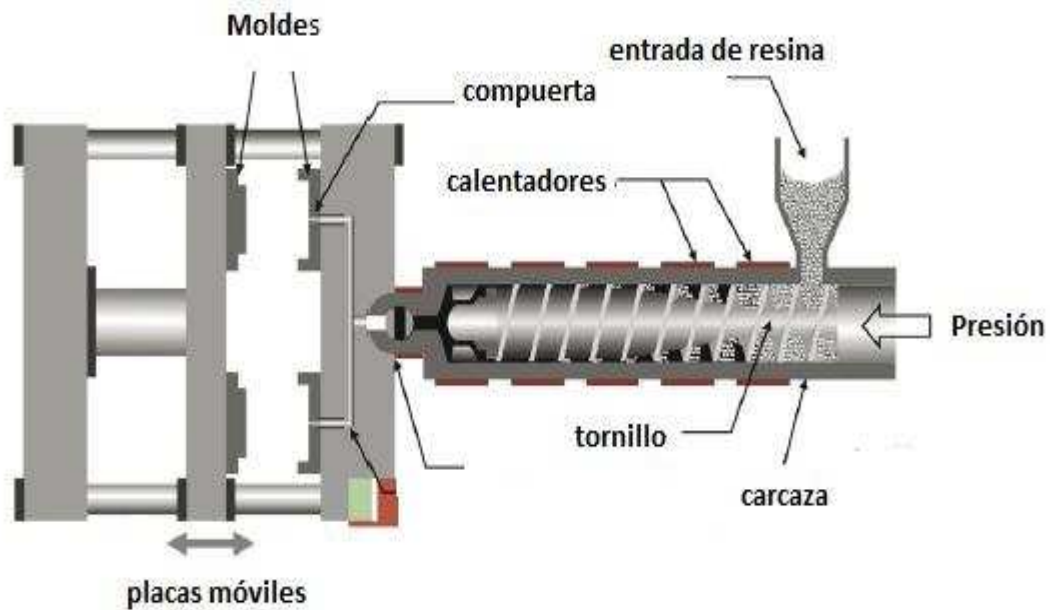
Componentes principales de una máquina para moldeo por inyección.
